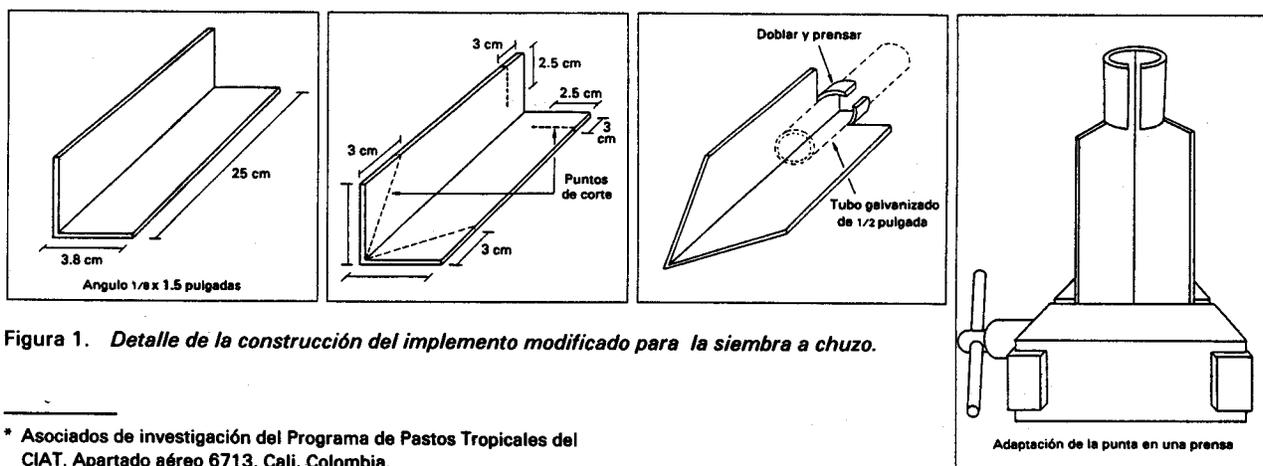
Detalle de la construcción del implemento modificado para la siembra a chuzo.
